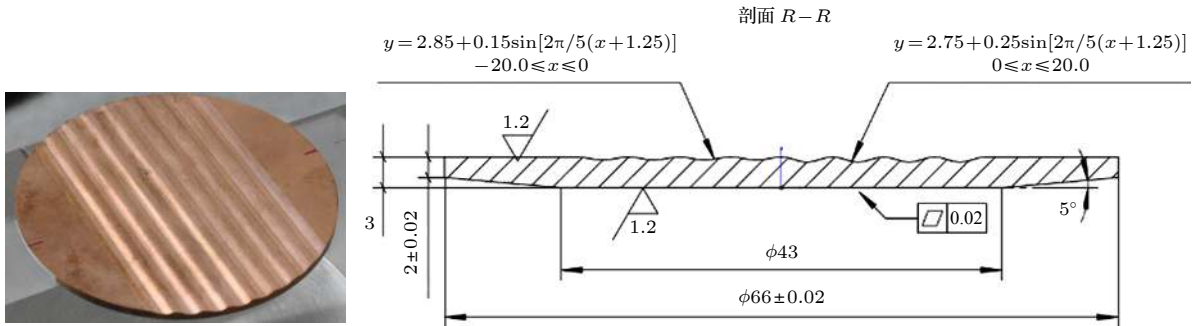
预制初始扰动的高纯铜样品实物图与剖面图 (单位: mm)
